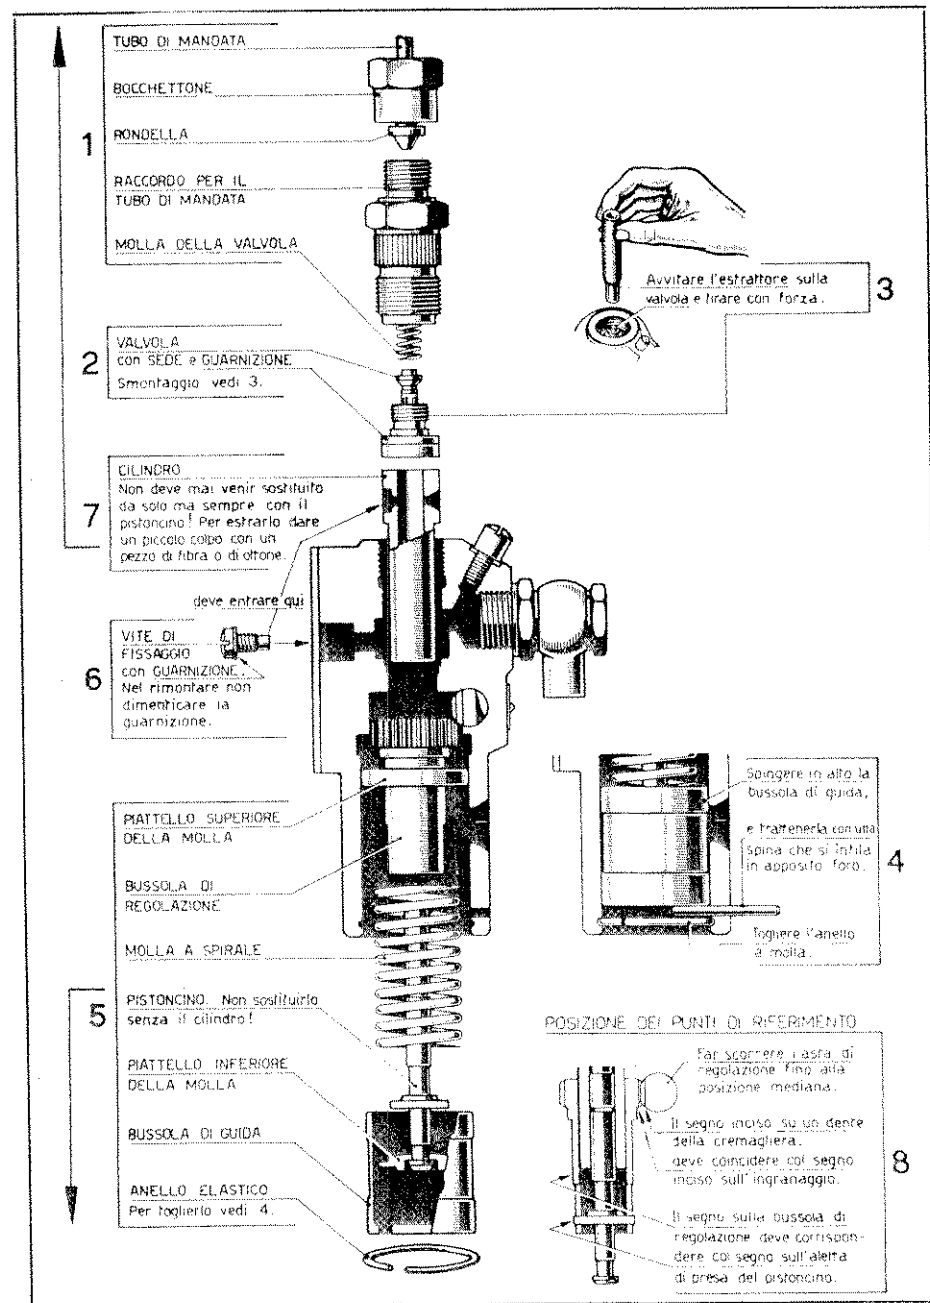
Istruzioni per lo smontaggio e il rimontaggio della pompa iniezione
